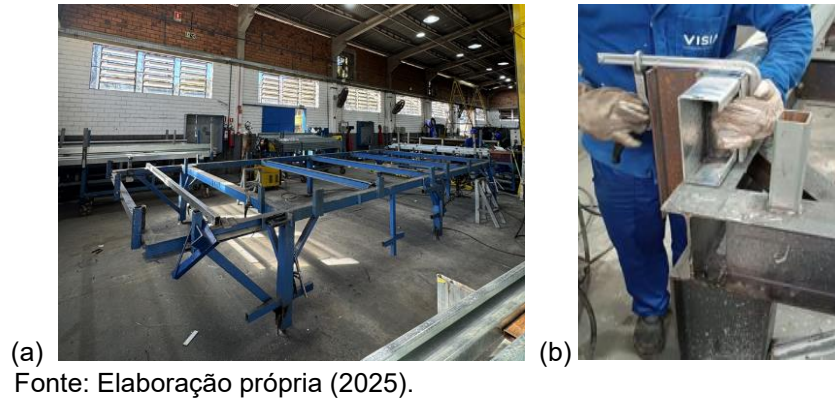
Perfis transversais: (a) execução do reforço central; (b) execução do reforço de extremidade no perfil transversal de piso
